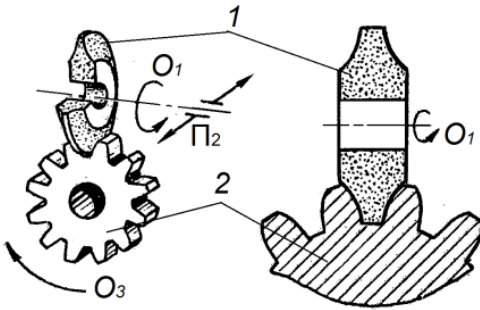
Схема шліфування зубів методом копіювання
